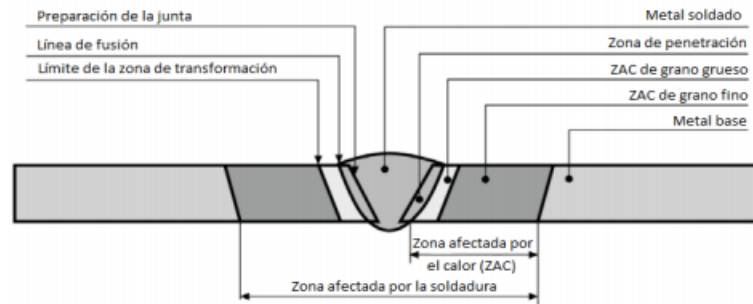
Zonas presentes en la soldadura[25]
